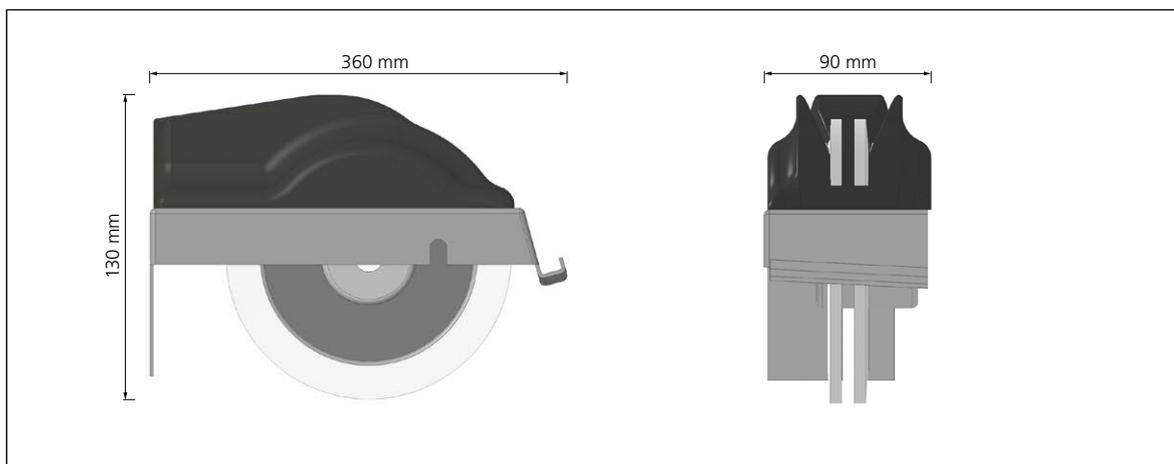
Vue latérale et vue de face du HV 150 (dimensions en mm)
